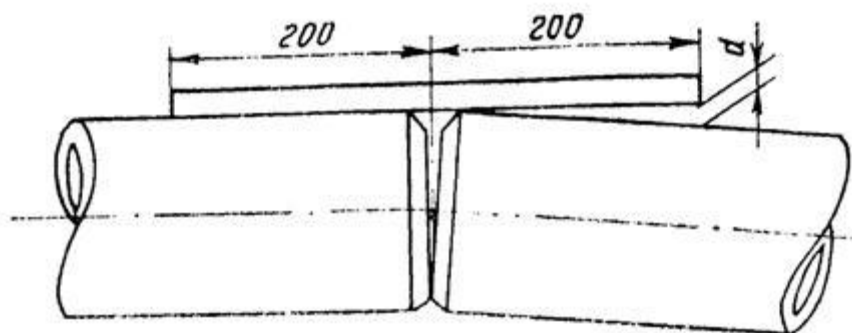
Проверка прямолинейности стыка элементов перед сваркой
